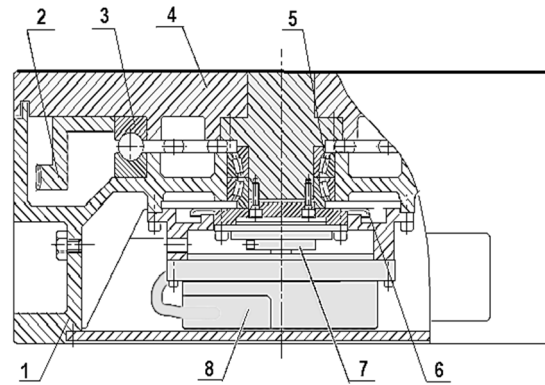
Поворотний привід з черв'ячною передачею
